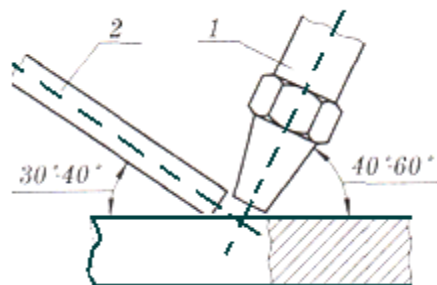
Схема перемещения горелки и прутка (левое):
